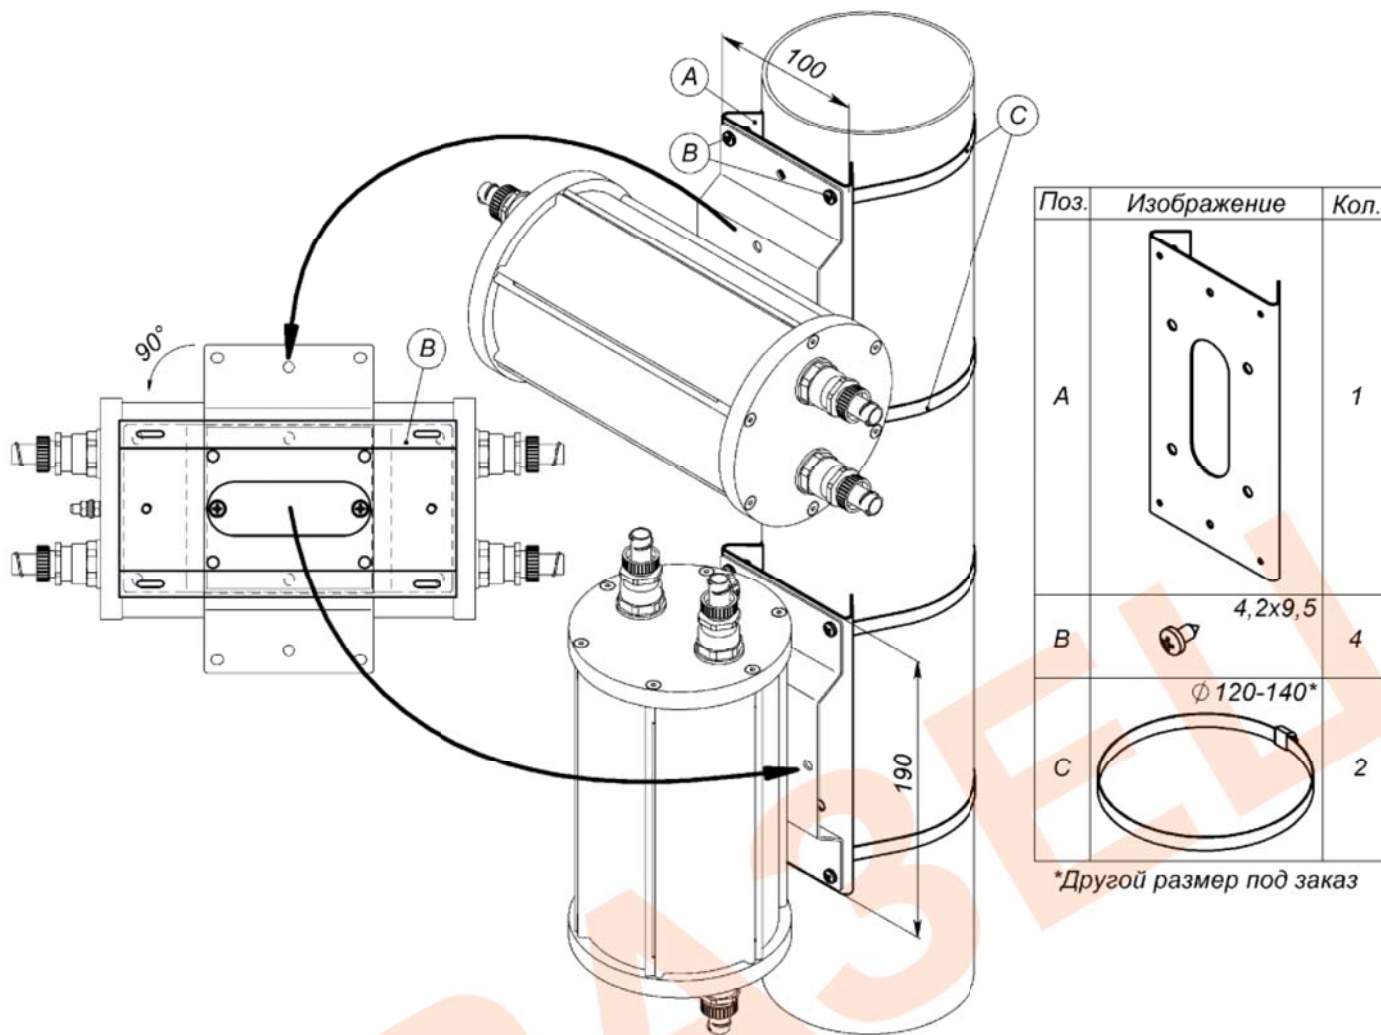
Монтаж кронштейна КС-1 на опору (круглую или квадратную)
